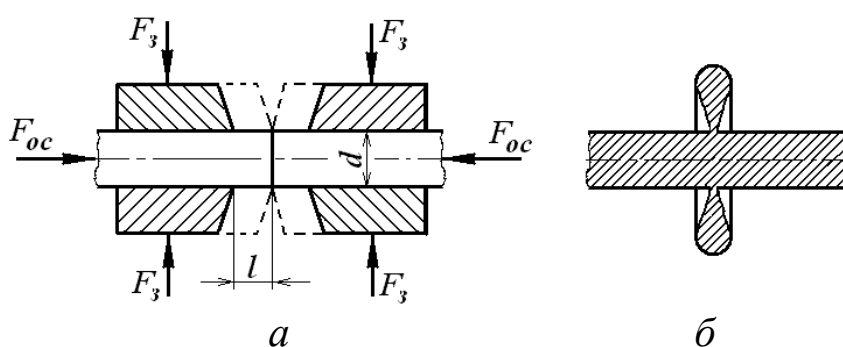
Схема процесса стыковой сварки (а) и вид соединения (б)
